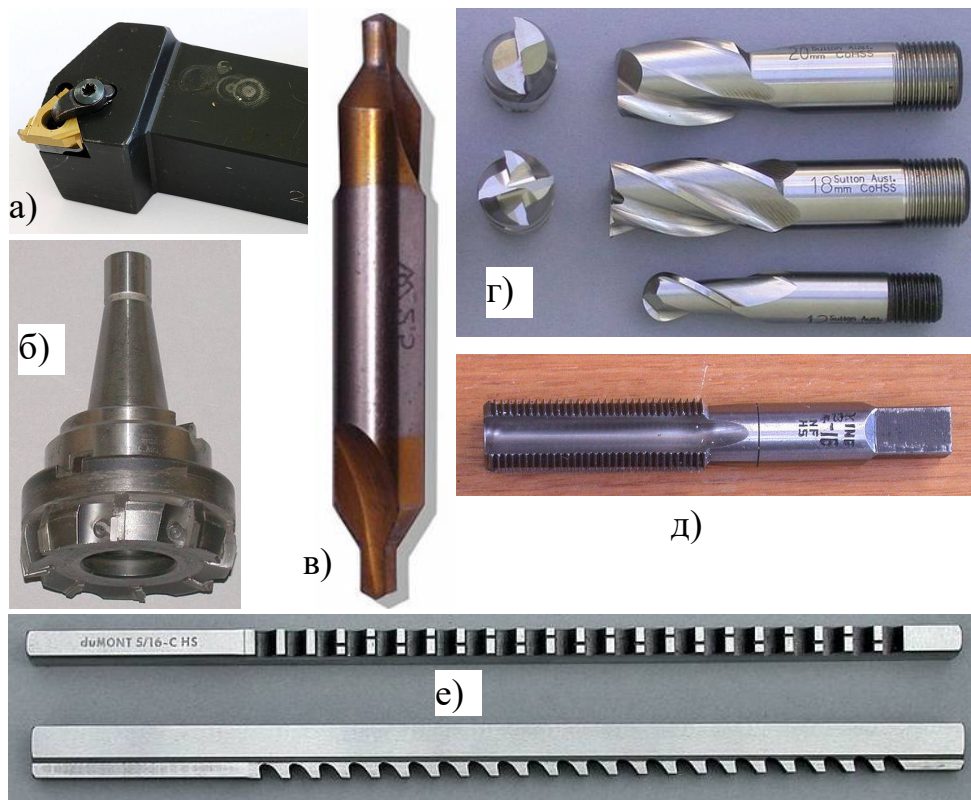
Сучасні різальні інструменти: а – прохідний різець з твердосплавною пластиною; б – торцева фреза; в – центрувальне свердло; г – кінцеві фрези; д – мітчик; е – шпонкові протяжки
